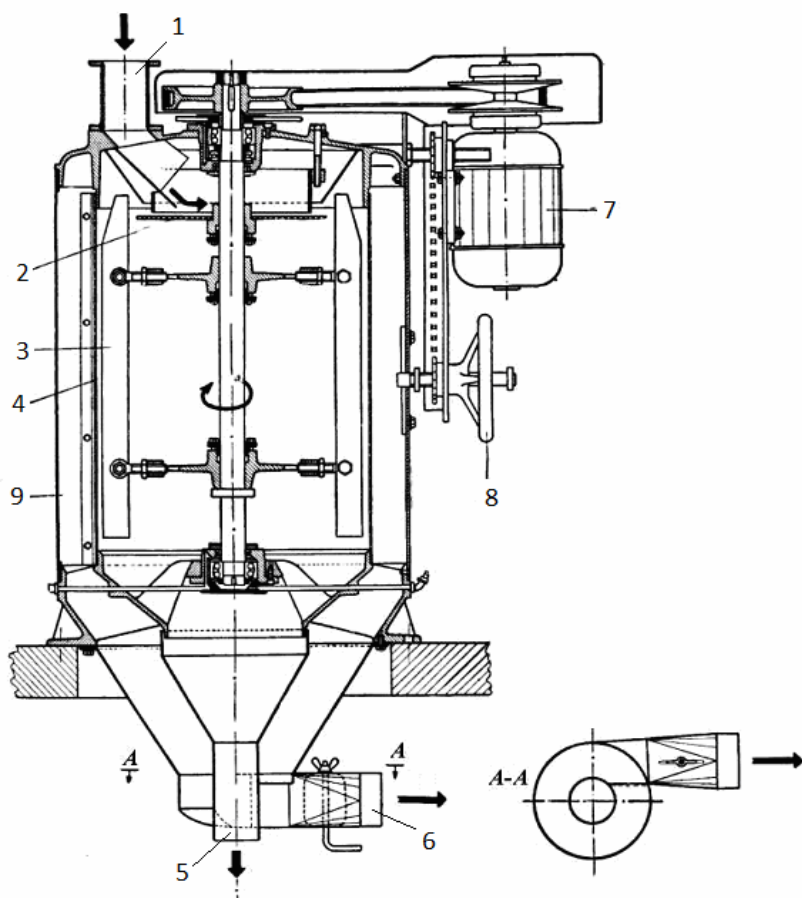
Schema unui degerminator cu rotor vertical: 1- gură de alimentare; 2- disc rotativ distribuitor; 3- palete rotor; 4- mantă cilindrică perforată; 5- gură evacuare; 6- racord admisie aer aspirat; 7- electromotor acționare; 8- variator de turație; 9- carcasă degerminator.
